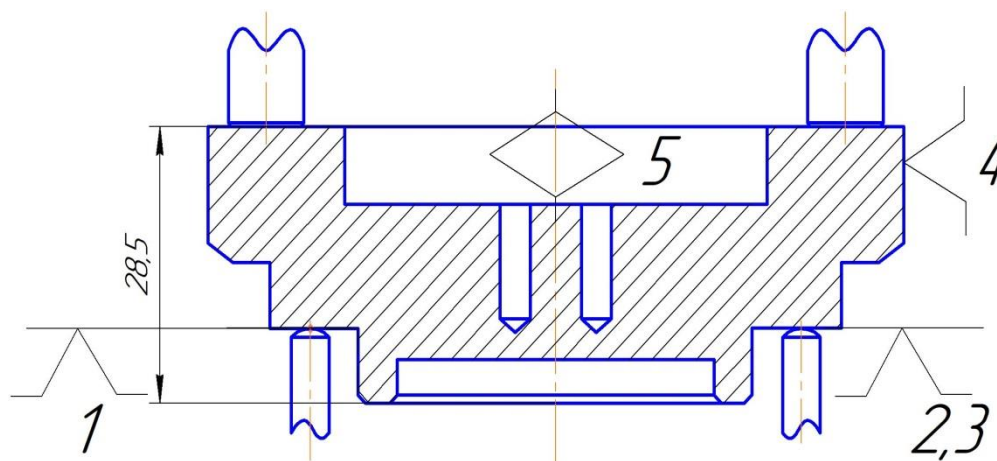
Принципиальная схема зажима заготовки в приспособлении с указанием мест приложения силы зажима.
